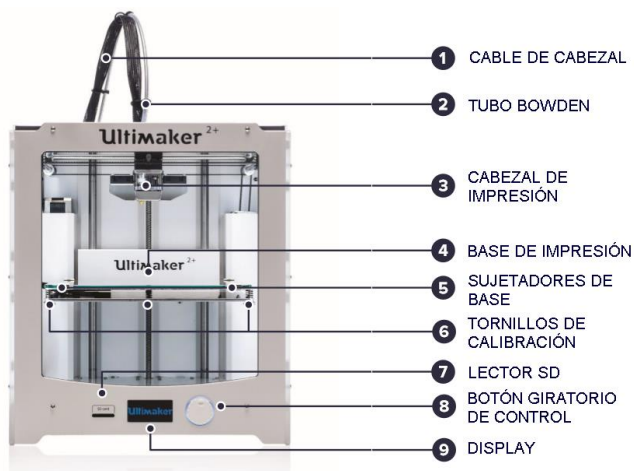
Ultimaker parte frontal y componentes (Ultimaker, 2017)
